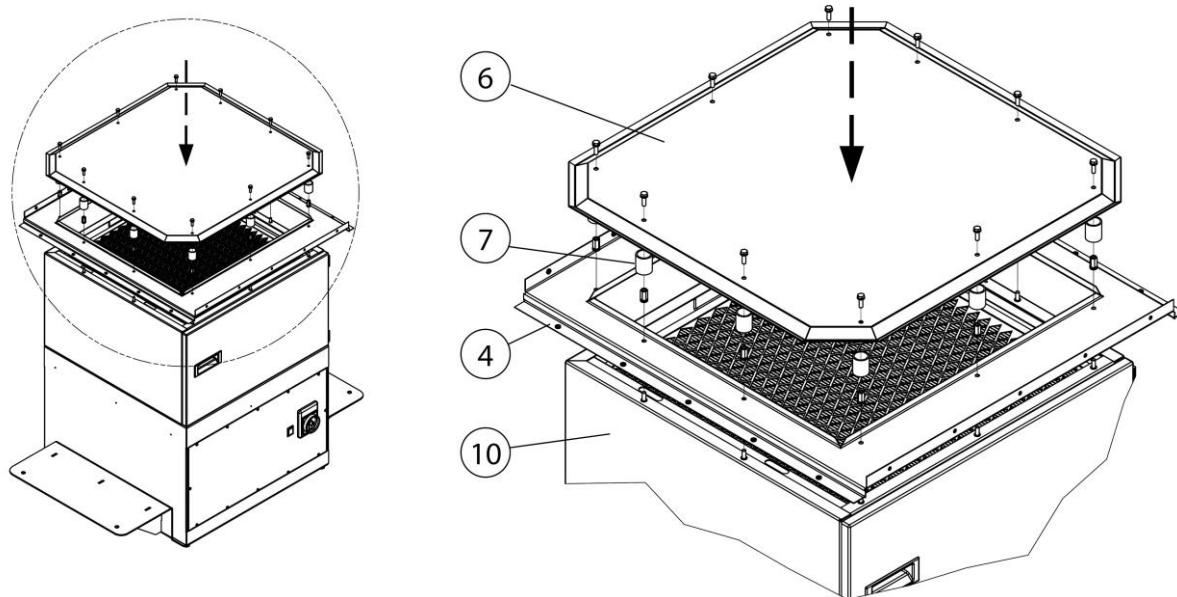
Montaggio - Telaio di appoggio + lamiera anti-scintille
